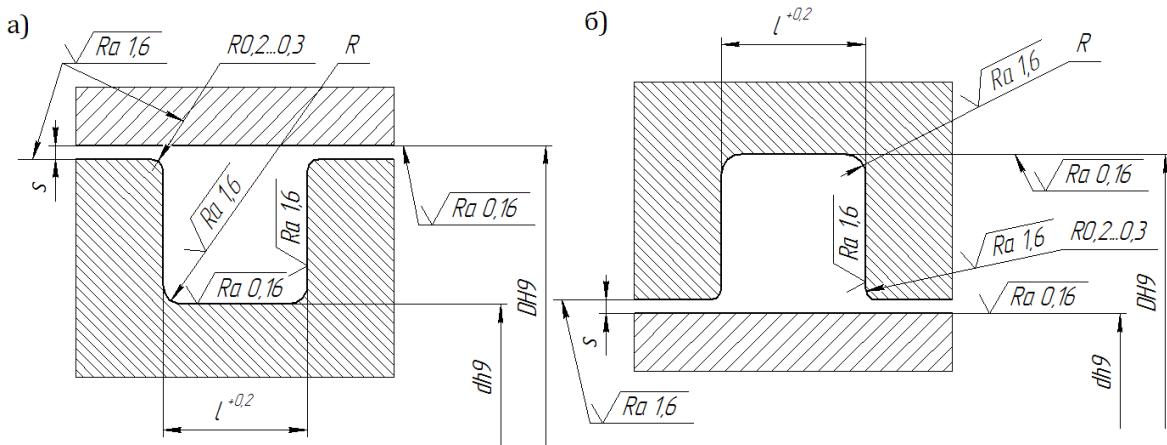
Канавки под уплотнение: а – поршня, б – штока
